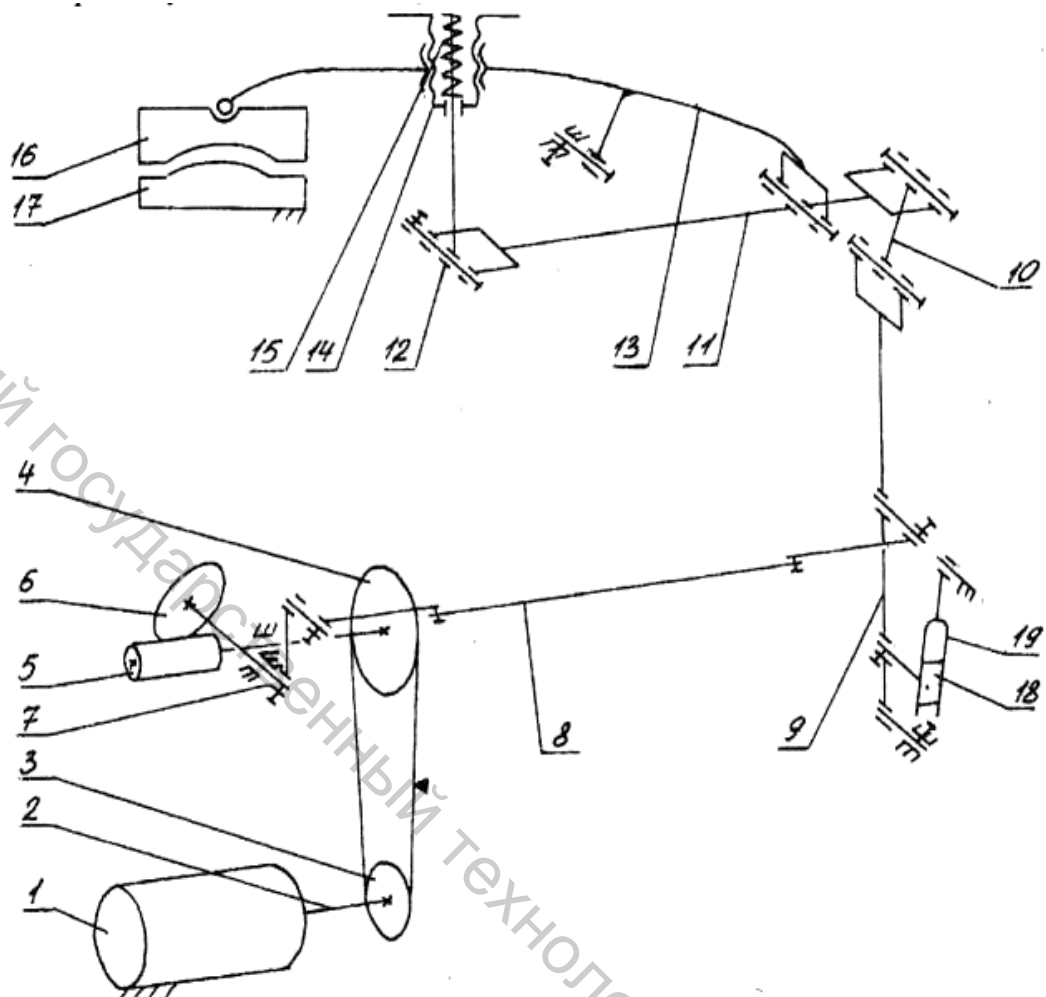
Кинематическая схема механизма привода подушки
